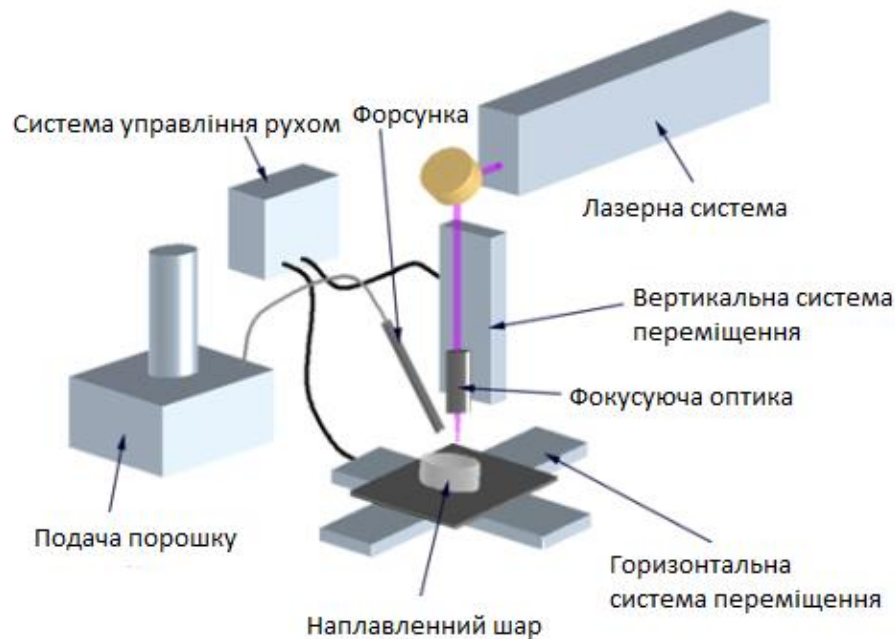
Схема обладнання для газопорошкового лазерного наплавлення
